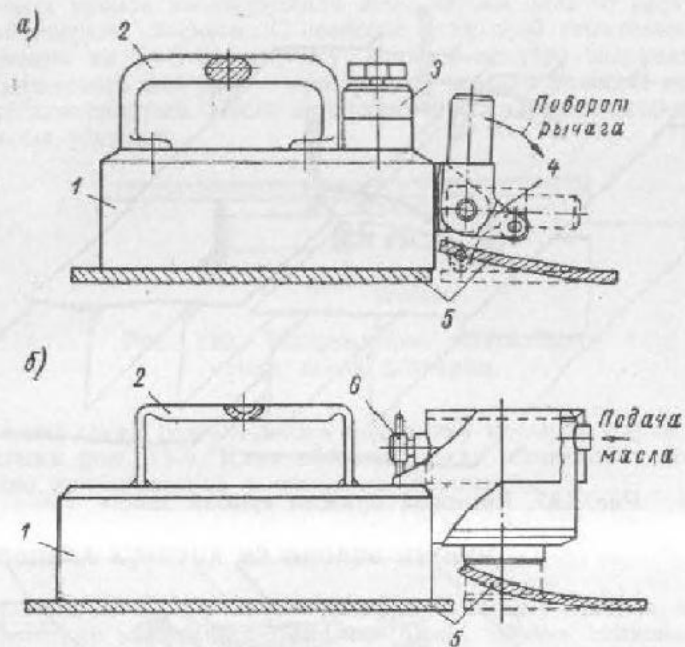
Сборочные приспособления с электромагнитами: а — с нажимным рычагом; б — с малогабаритным гидродомкратом.
